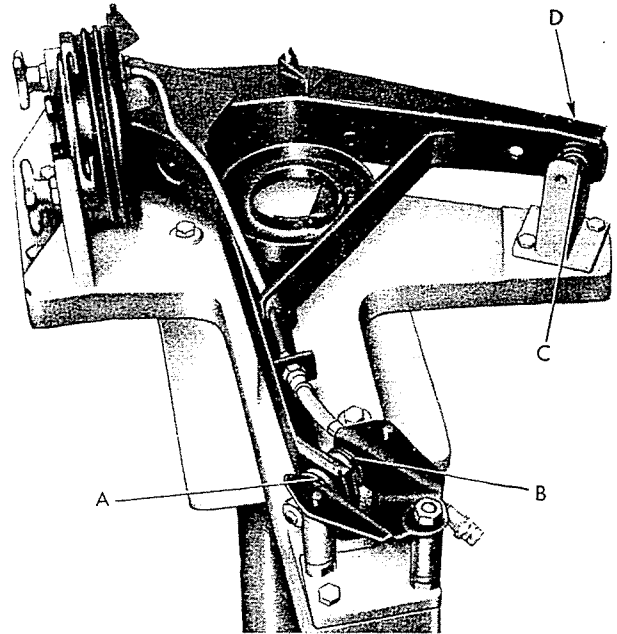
Einstellung des rechten Längslenkers auf dem Werkzeug A. 66064.
